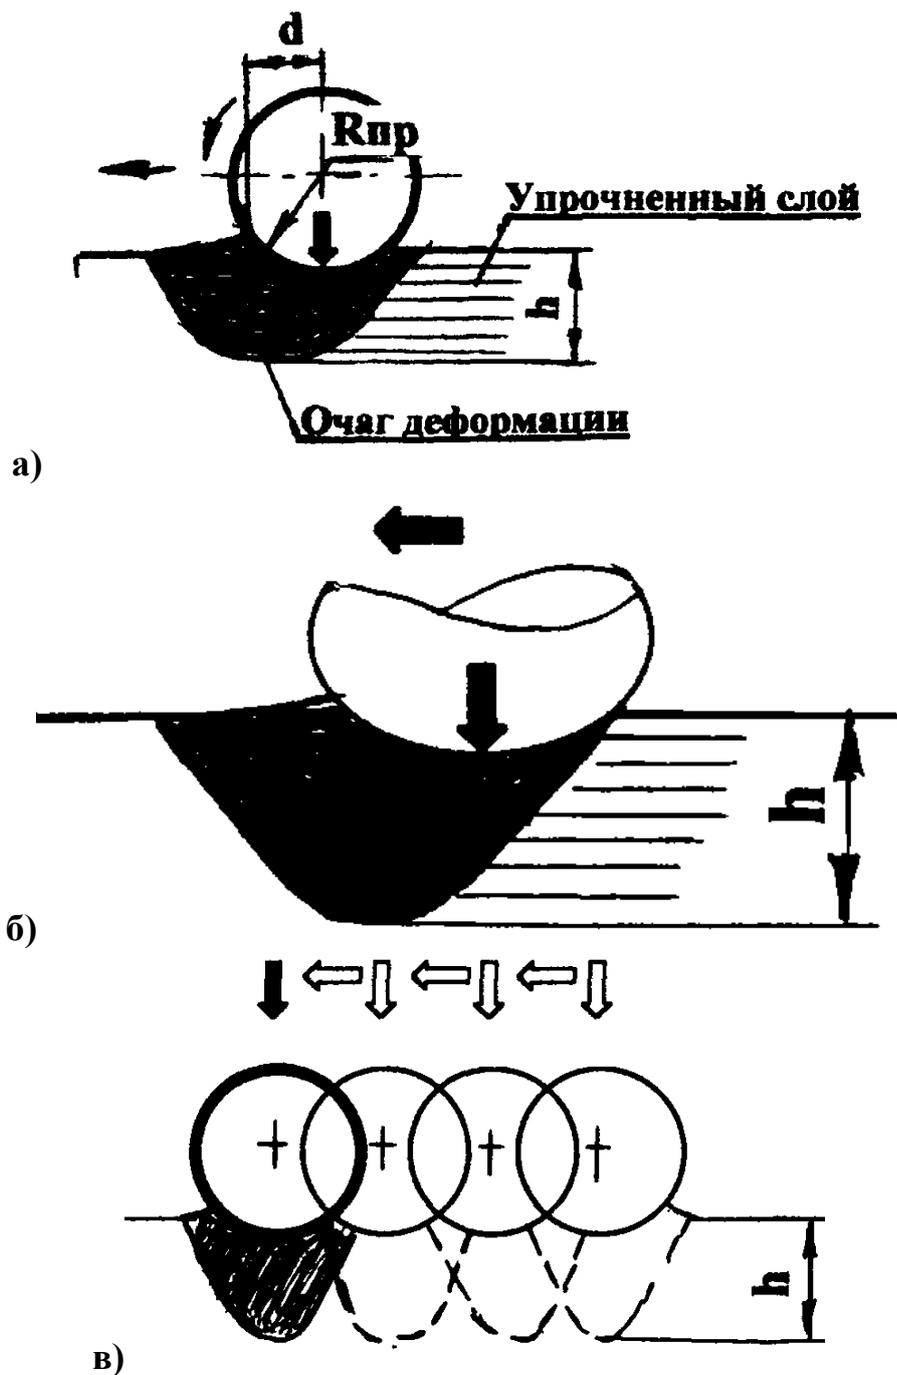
Основные схемы взаимодействия ДЭ с обрабатываемой поверхностью:
